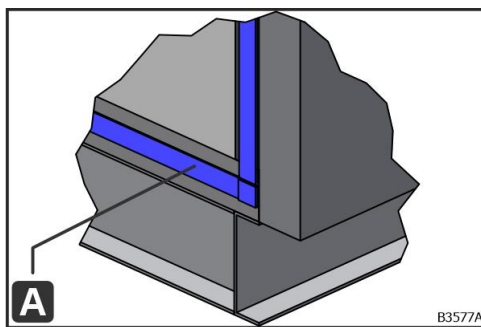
Fond du caisson recouvert de ruban adhésif (50 mm)
